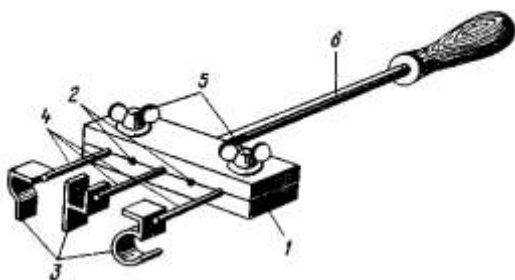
Приспособление для клеймения рыб: 1 – державка; 2 – отверстие для закрепления матриц; 3 – матрицы; 4 – штоки; 5 – винты; 6 – рукоятка
